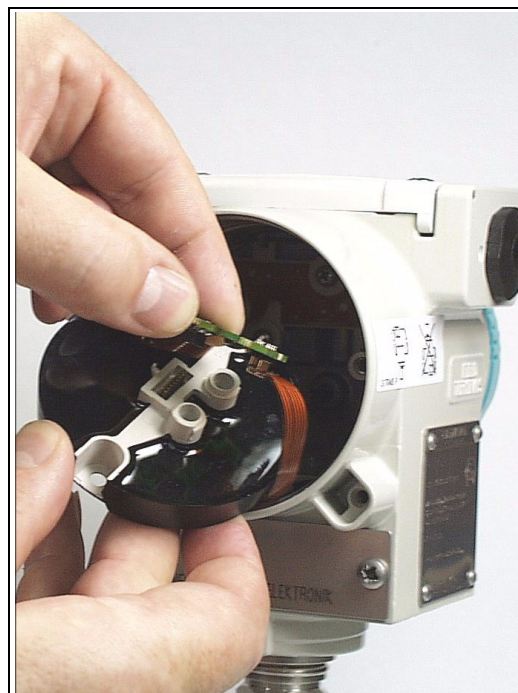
Aufstecken der Messzellenplatine ab Erzeugnisstand 30
